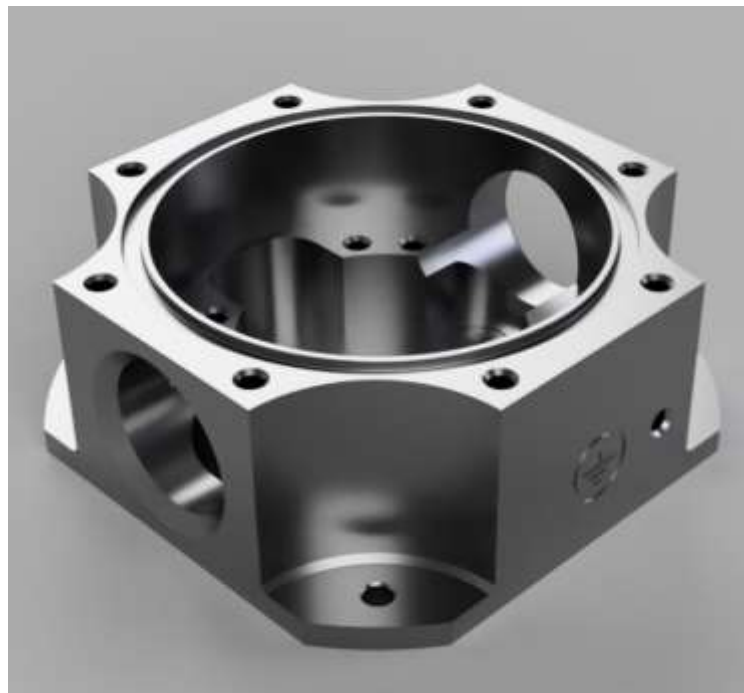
Тривимірний модель корпусу клемної коробки
